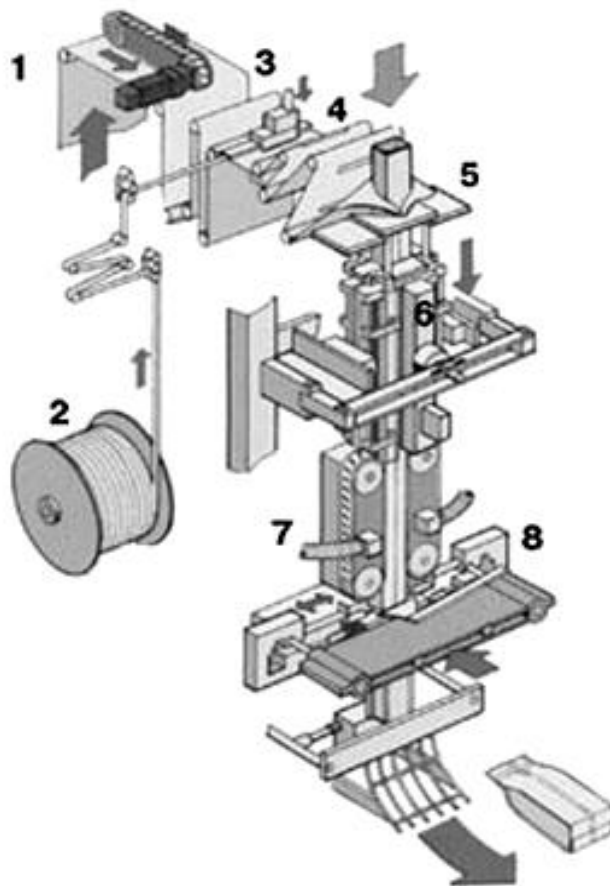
Принцип роботи вертикальної рукавної машини ROBERT BOSCH періодичної дії з протягувальними вакуумними пасами, зварювання кантів та вставка ZIP-застібки (GMBH): 1 - подача пакувального матеріалу; 2 - рулон із ZIP-застібкою; 3 - вузол зварювання (склеювання) ZIP-застібки; 4 - зварювання (склеювання) ZIP-застібки; 5 - формувальний комірець; 6 - повздовжня термозварювальна колодка; 7 - вакуумні потягувальні паси; 8 - поперечні термозварювальні колодки.
